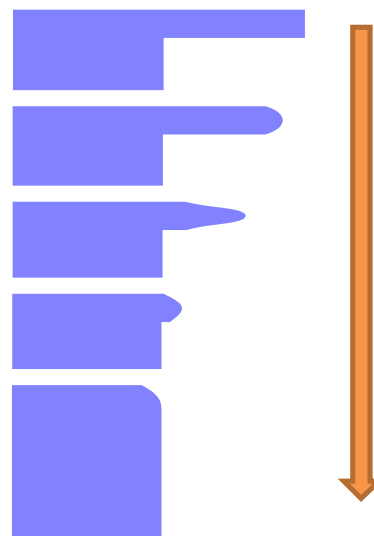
Картина оплавления заусенца и скругления кромки детали
